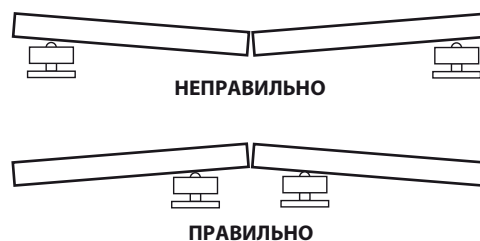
Установка трубных опор для предотвращения защемления отрезного диска трубой
